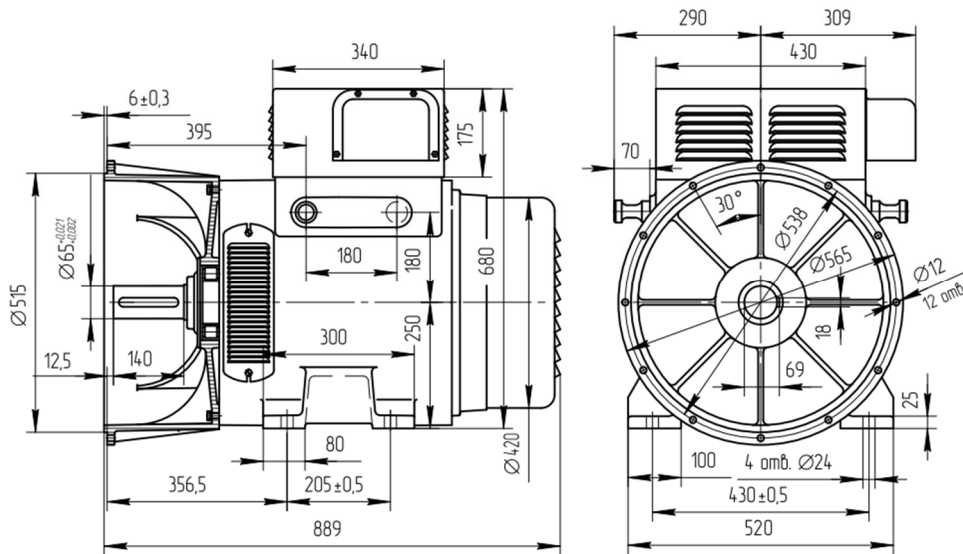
Габаритные, установочные и присоединительные размеры генератора ГС 250-60/4
